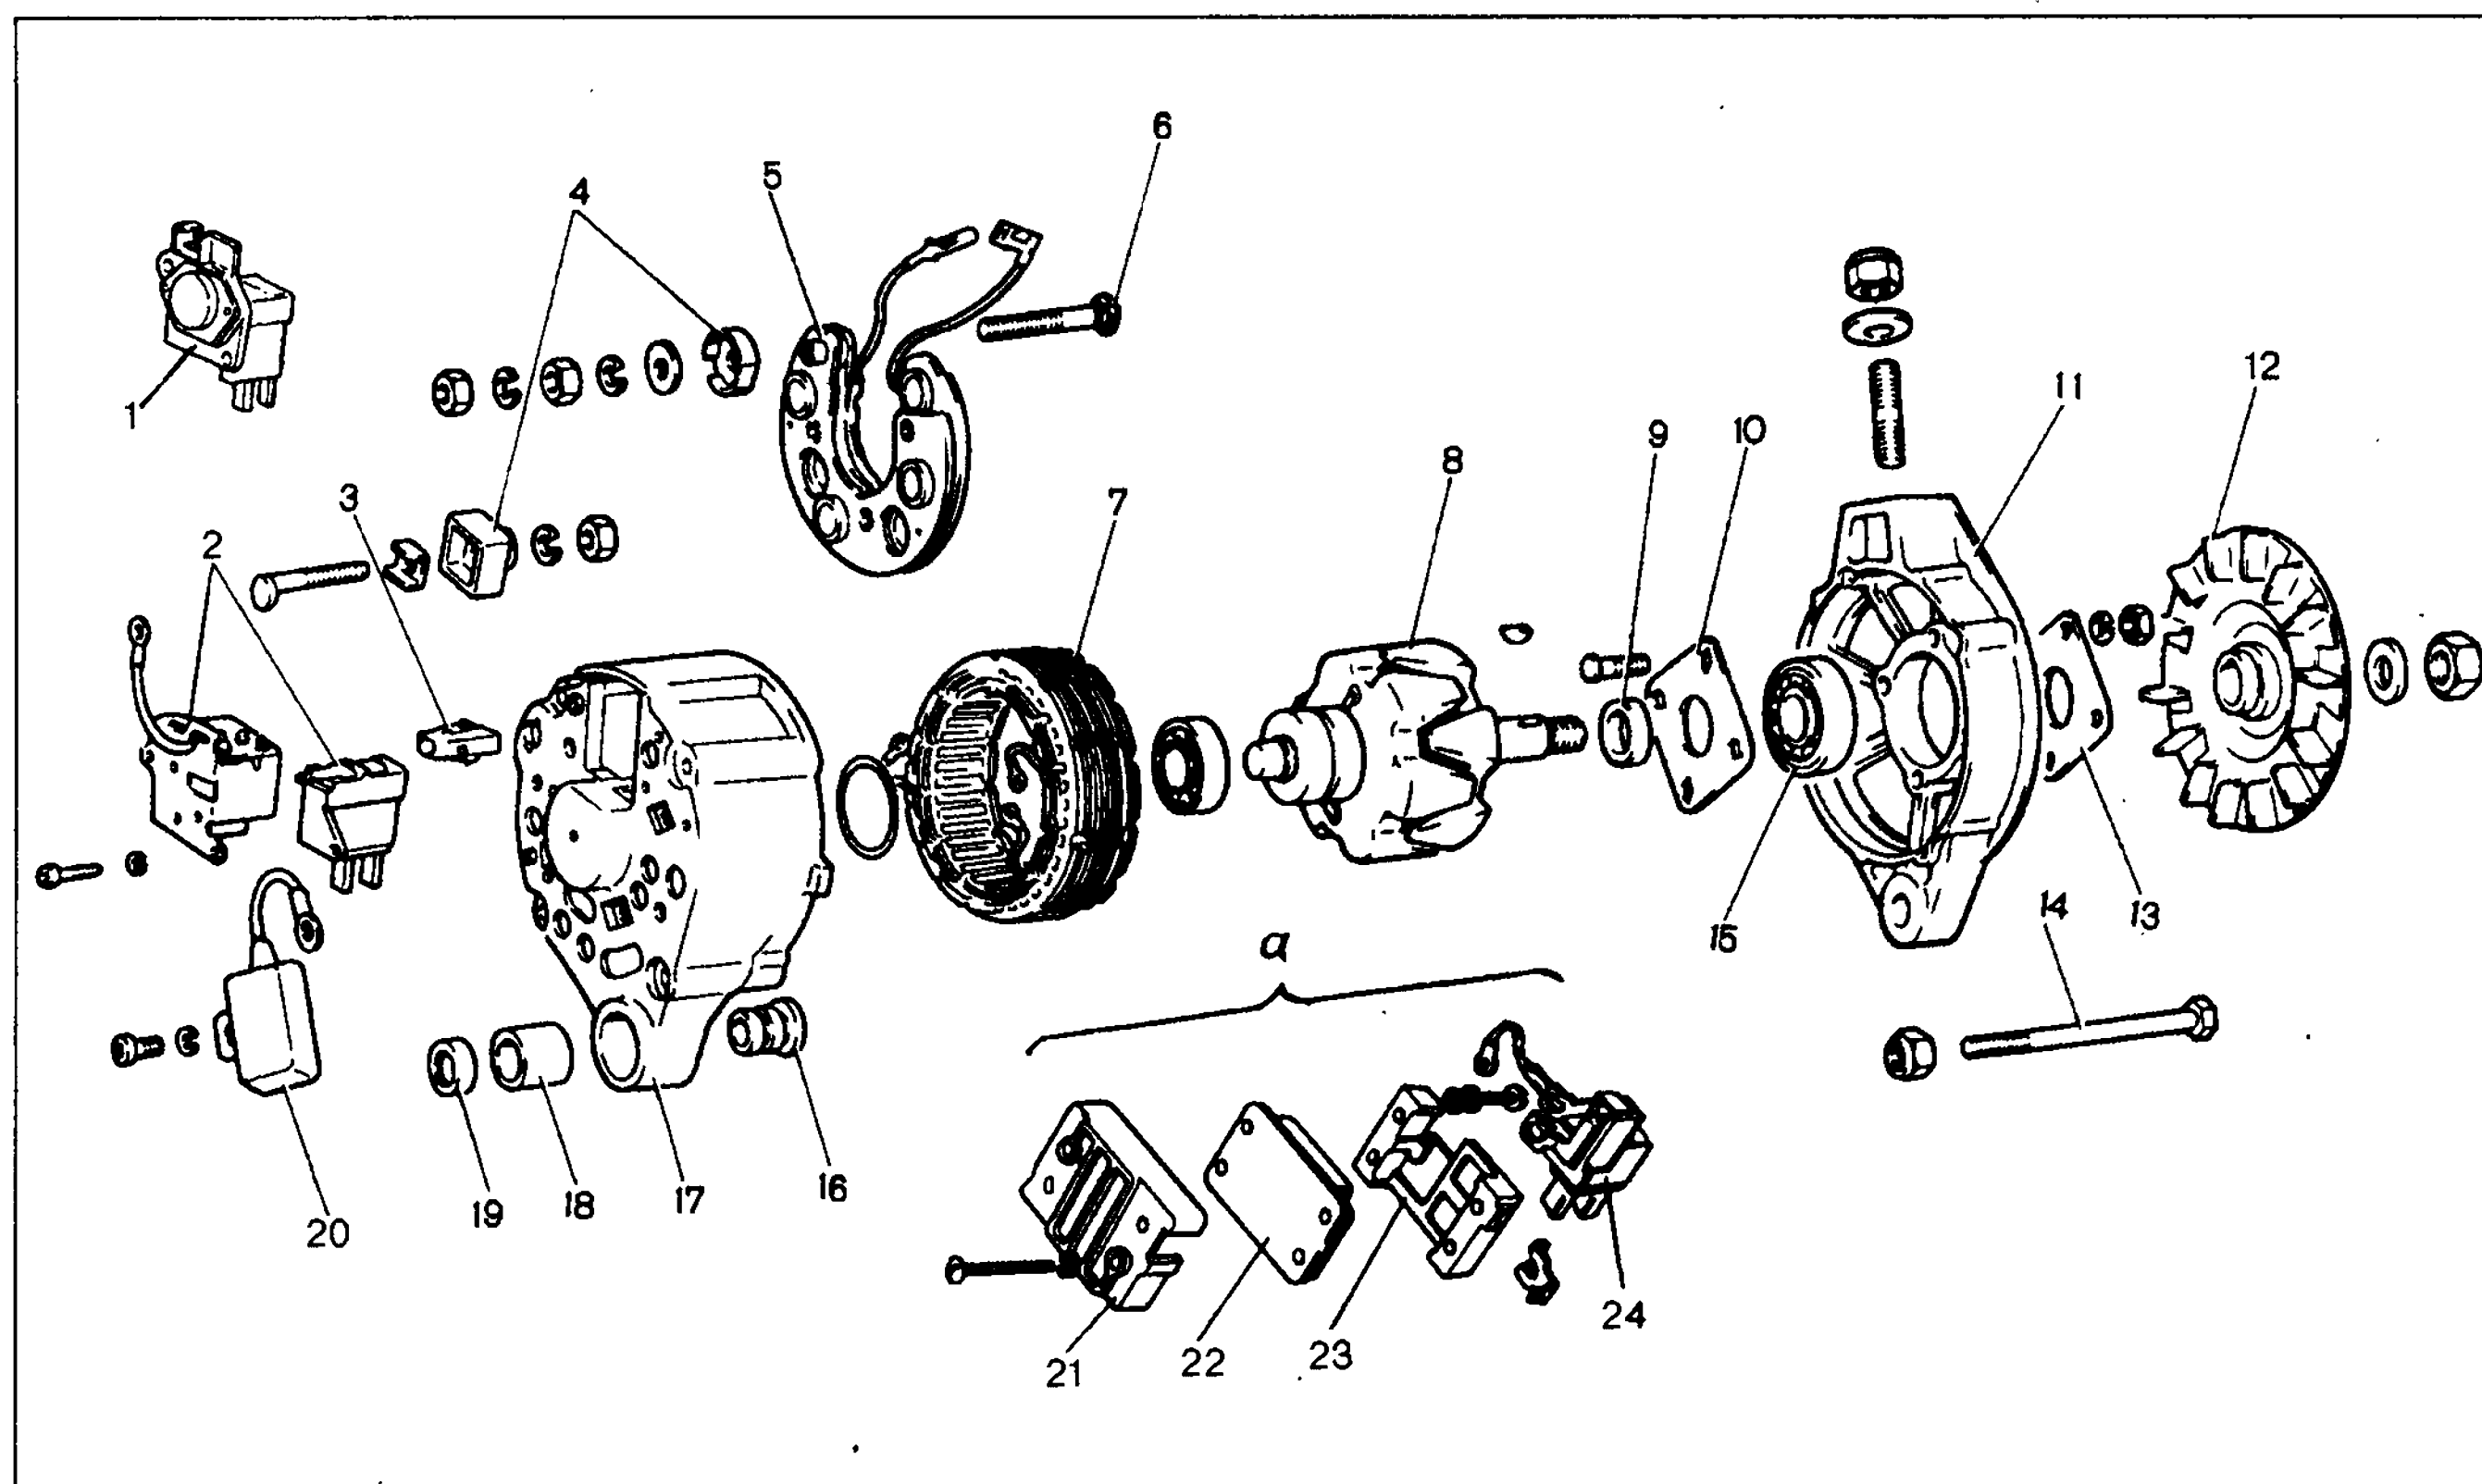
Детали генератора 37.3701 (а — детали передней части генератора Г-222):
